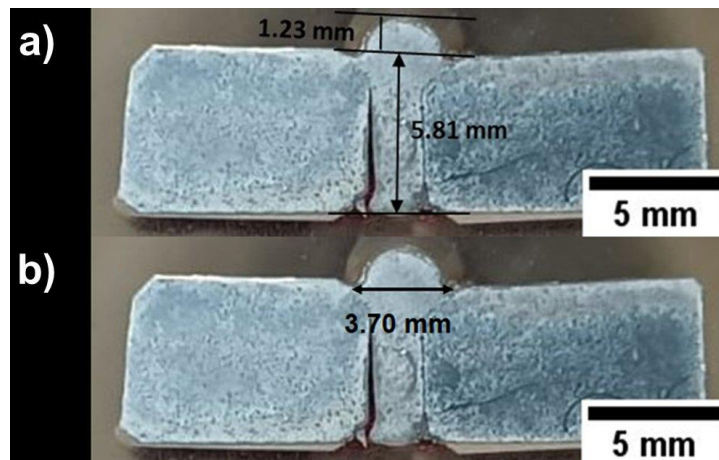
78 Geometría del cordón de soldadura número 21, cuyos valores son a) 1.23 mm de concavidad de la corona y 5.81 mm de penetración y b) 3.70 mm de ancho del cordón de soldadura.
